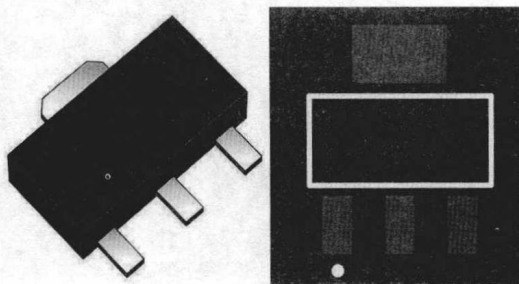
表面安装式封装的元件外形及其 PCB 焊盘
